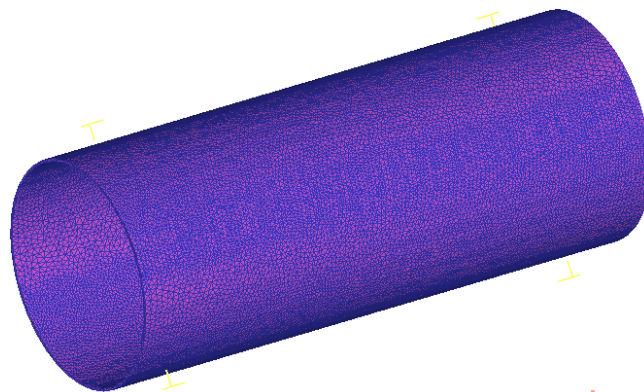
Сеточный аналог трубчатой заготовки
